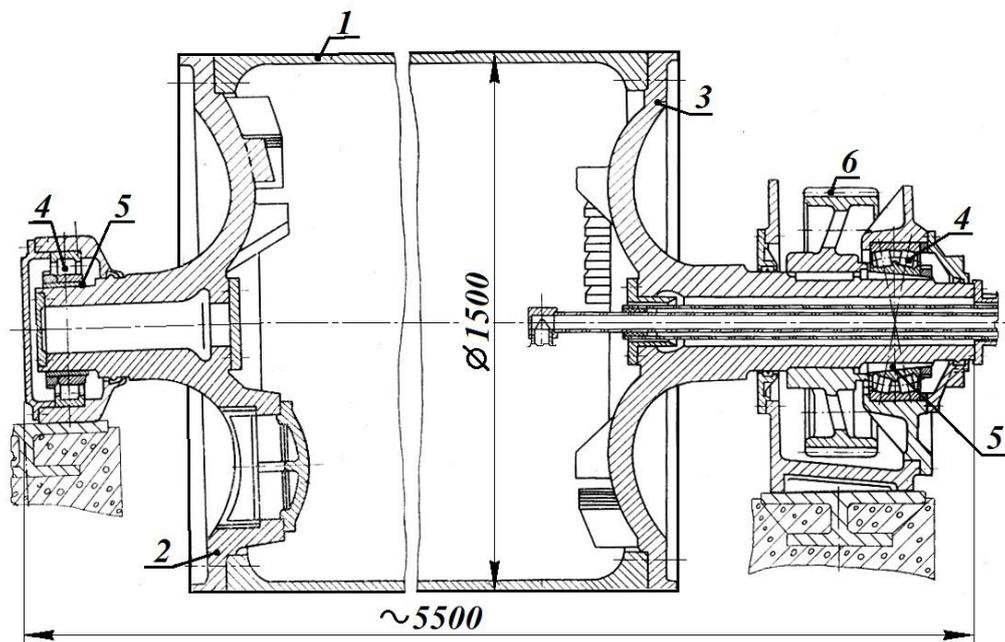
Сушильный цилиндр: 1 – цилиндр; 2 – крышка-цапфа лицевой стороны; 3 – крышка-цапфа приводной стороны; 4 – подшипник качения; 5 – разжимная втулка; 6 – шестерня
